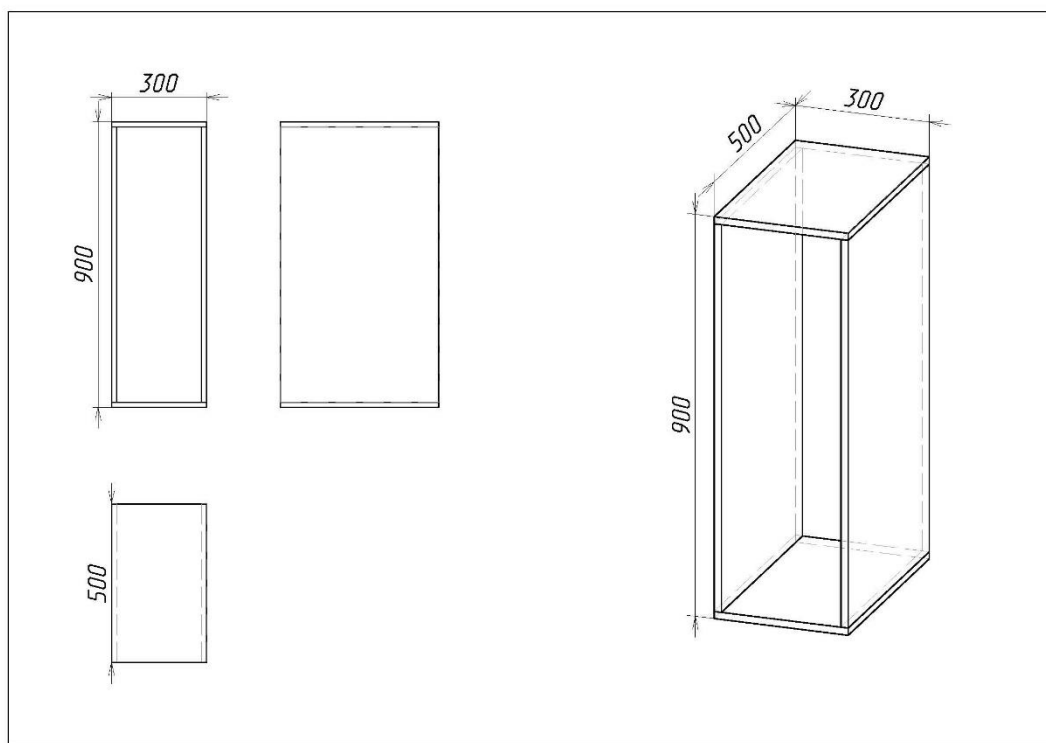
Корпус – крышка и дно накладные (БМ)
